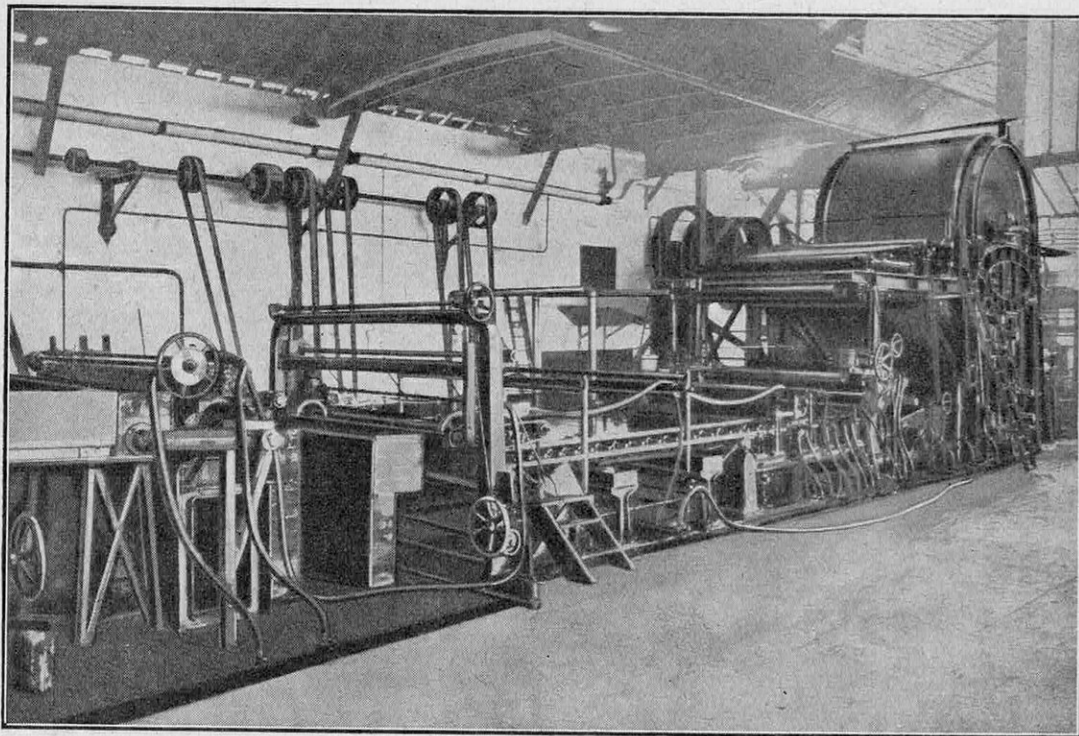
VUE DE LA MACHINE A PAPIER YANKEE DU COTÉ OU ARRIVE LA PATE HUMIDE. LE CYLINDRE SÈCHEUR EST VISIBLE A L'ARRIÈRE-PLAN
